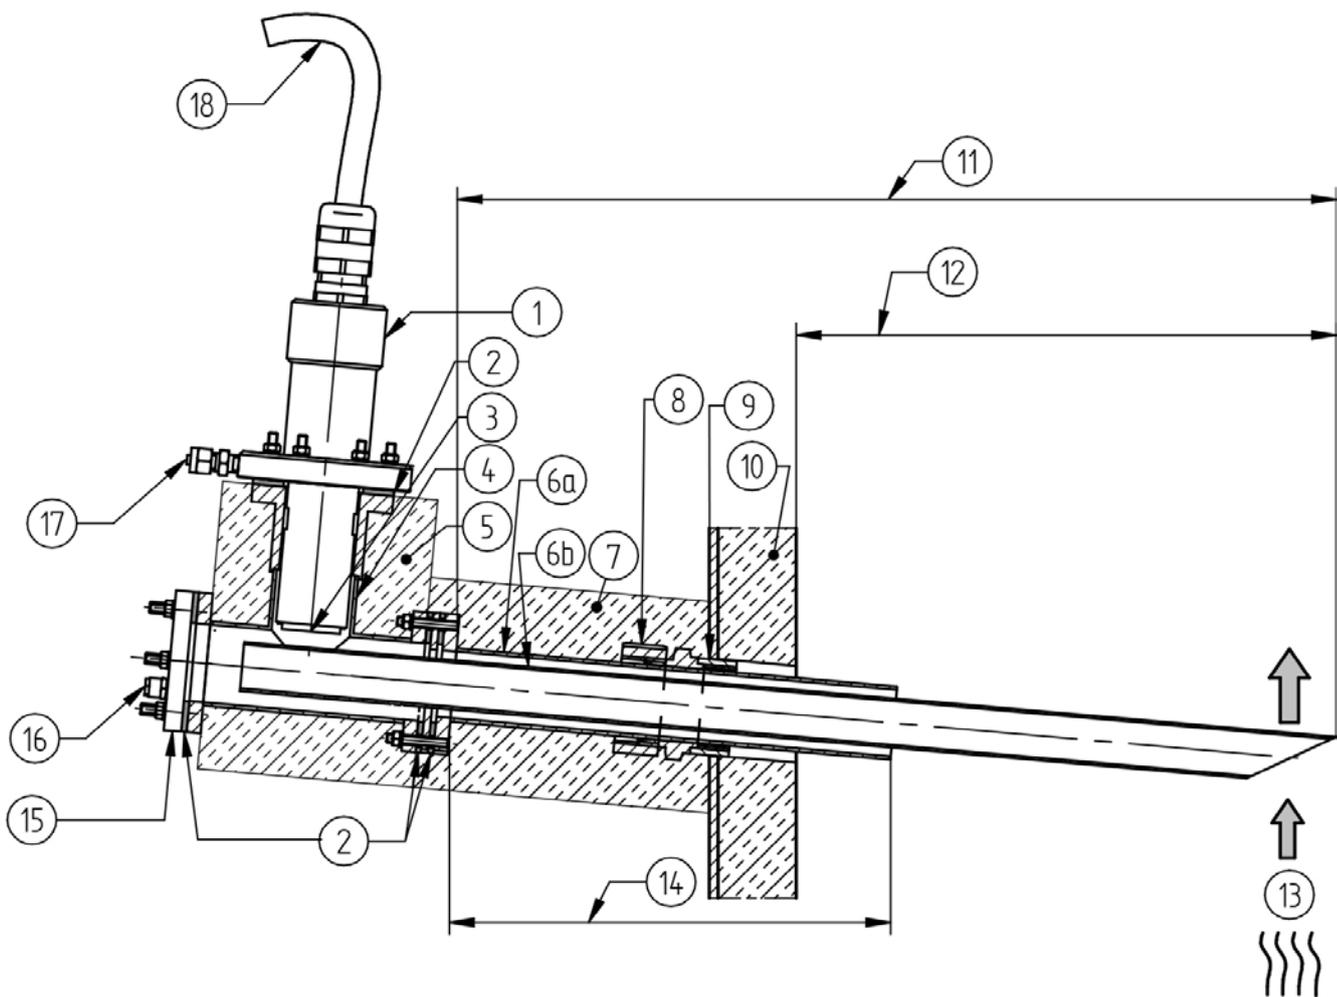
Ex-Sonde mit GED FLEX aus Kanthal oder AL203 mit T-Adapter
